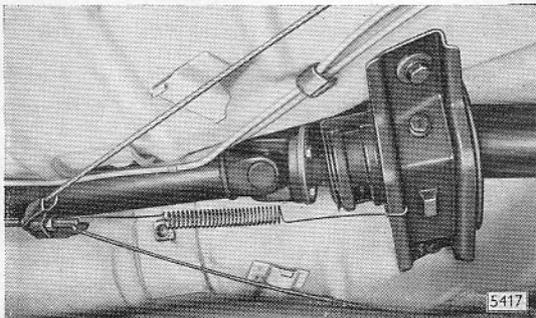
Anordnung Bremsseilausgleich und Gelenkwellenbefestigung
